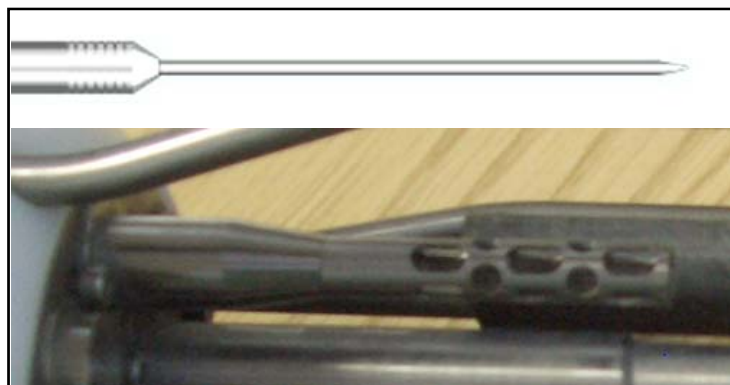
Esquema constructiu del sensor (superior) i fotografia del conjunt montat al perfilador.
